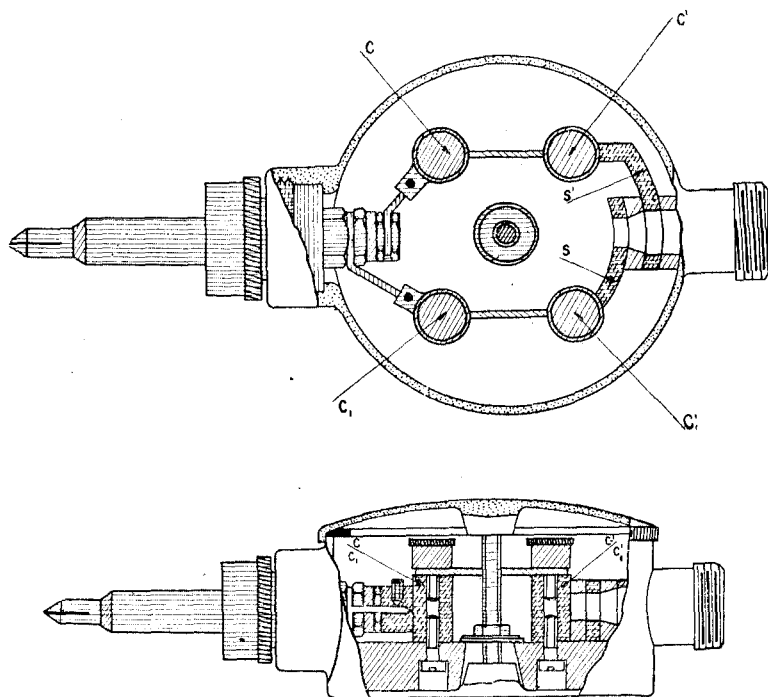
Caja metálica corta circuitos.—Planta y corte horizontal; vista y corte vertical.
